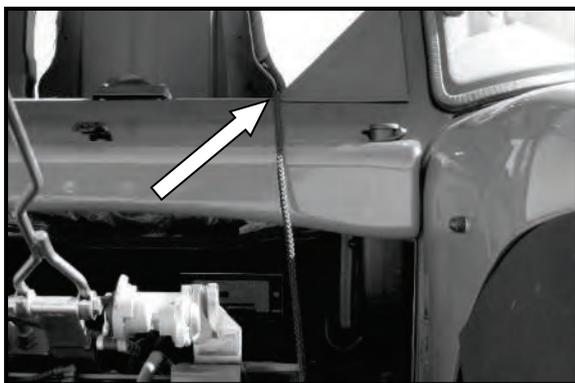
El cable de tracción está instalado en la cabina del tractor
